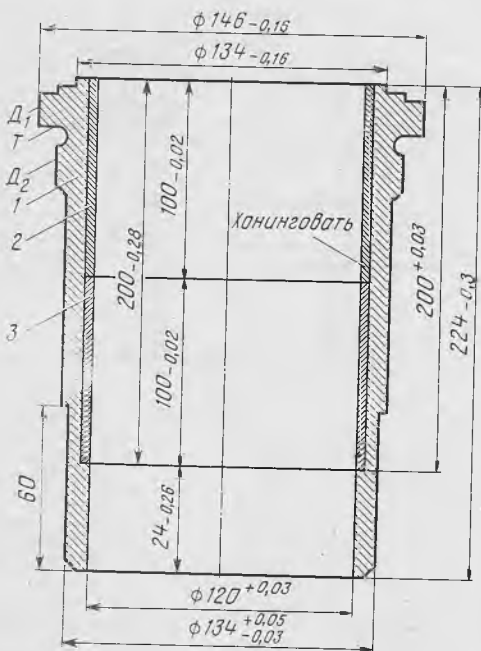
Геометрические размеры гильзы цилиндров КамАЗ-740, восстановленной под номинальный размер: D_1 , D_2 , T — посадочные поверхности гильзы цилиндров; 1 — гильза цилиндра; 2 и 3 — соответствующие верхняя и нижняя облицовочные пластины
